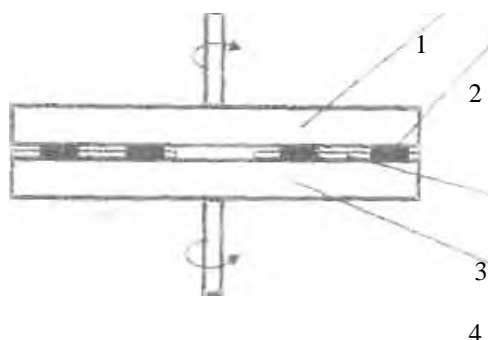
Шлифовка модулей на станке для двухсторонней шлифовки пластин: 1 - верхняя планшайба; 2 - модули; 3 - сепаратор; 4 - нижняя планшайба
